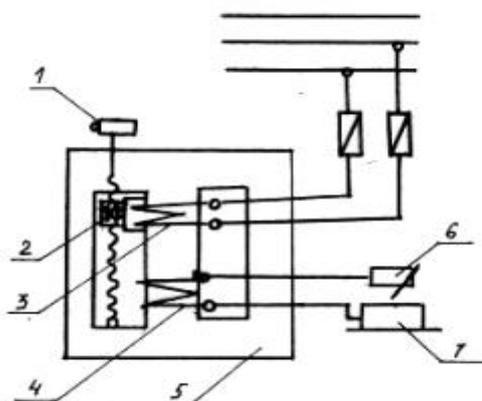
Схема сварочного трансформатора с подвижной катушкой:
